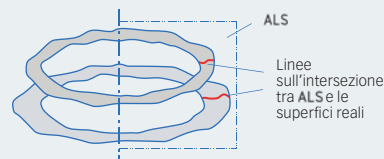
Linee di intersezione costruite dal piano ALS e dalle facciate reali dell'anello.
